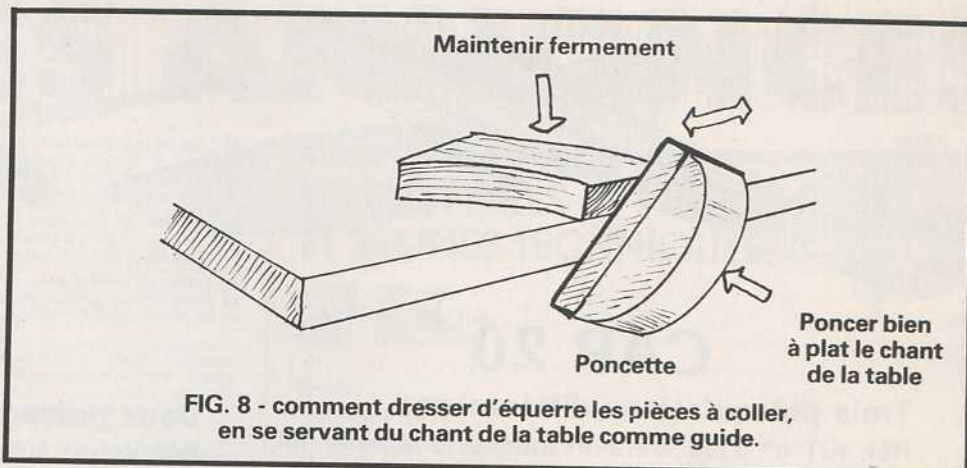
comment dresser d'équerre les pièces à coller, en se servant du chant de la table comme guide.
